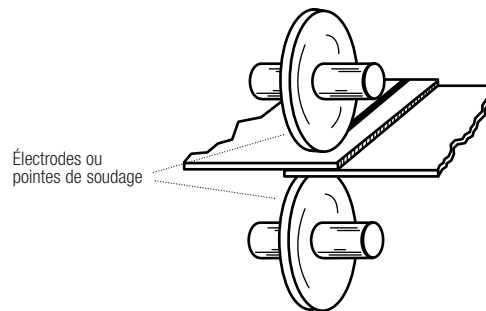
Soudage par résistance à la molette (RSEW)
